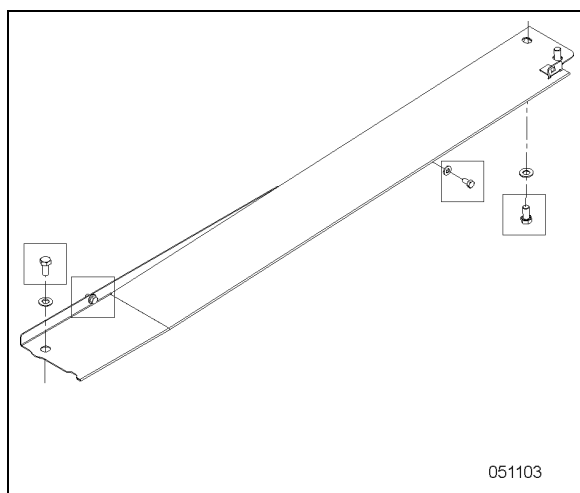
TORNILLOS DE MONTAJE DE LA PLACA PROTECTORA
